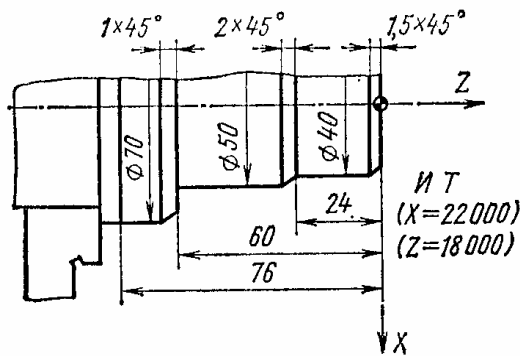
Эскиз заготовки (к заданию 16.8)
